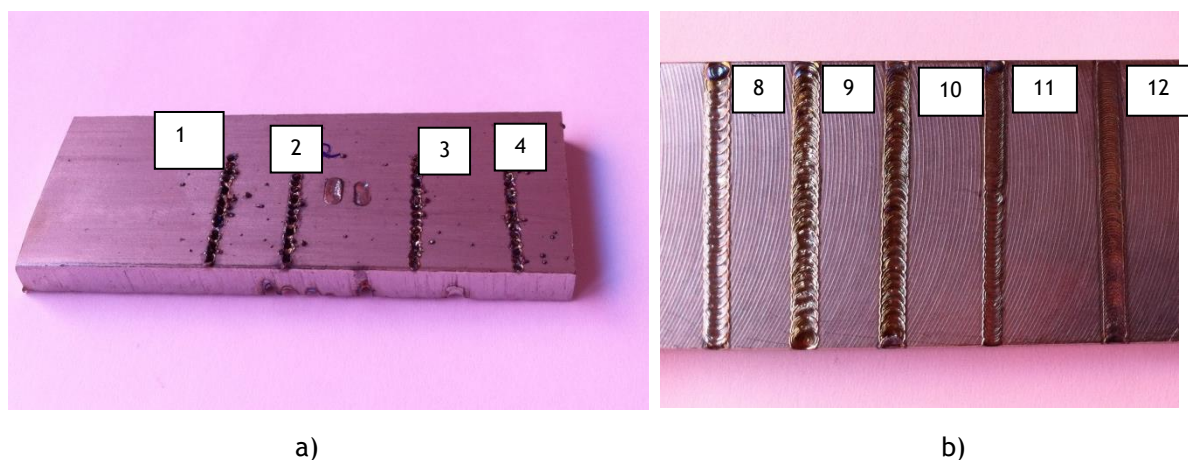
Aspeto dos cordões por soldadura laser na primeira fase: a) perfuração; b) soldadura por condução
